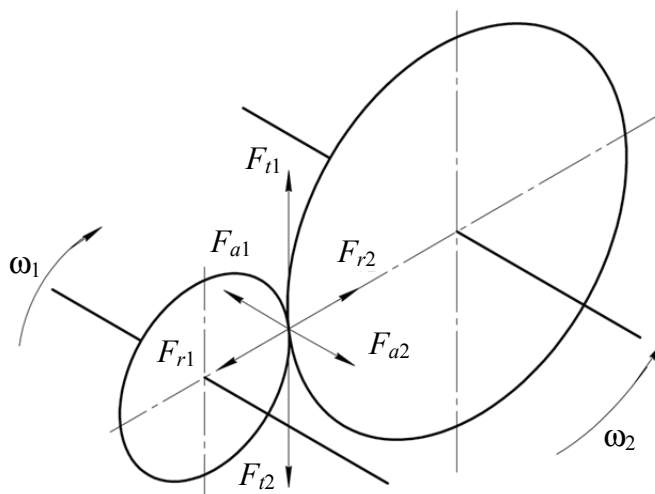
Схема сил в цилиндрической косозубой зубчатой передаче
